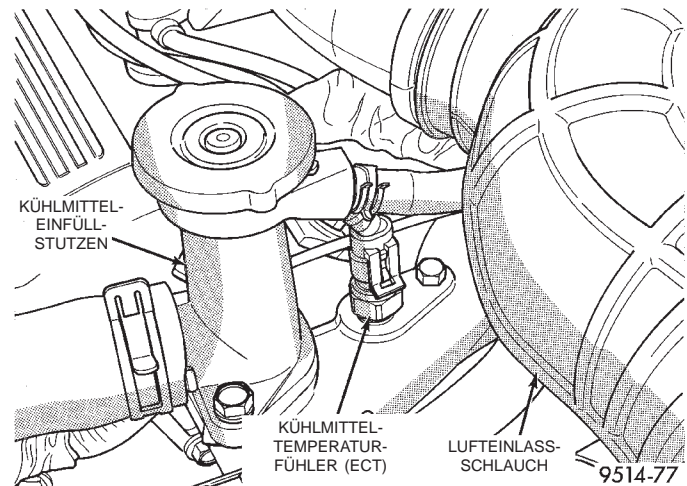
Kühlmittel-Temperaturfühler (ECT) — 2.5L-Motor
